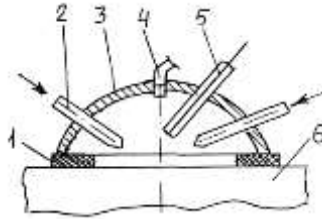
Схема электрогидравлической очистки крупных заготовок:
